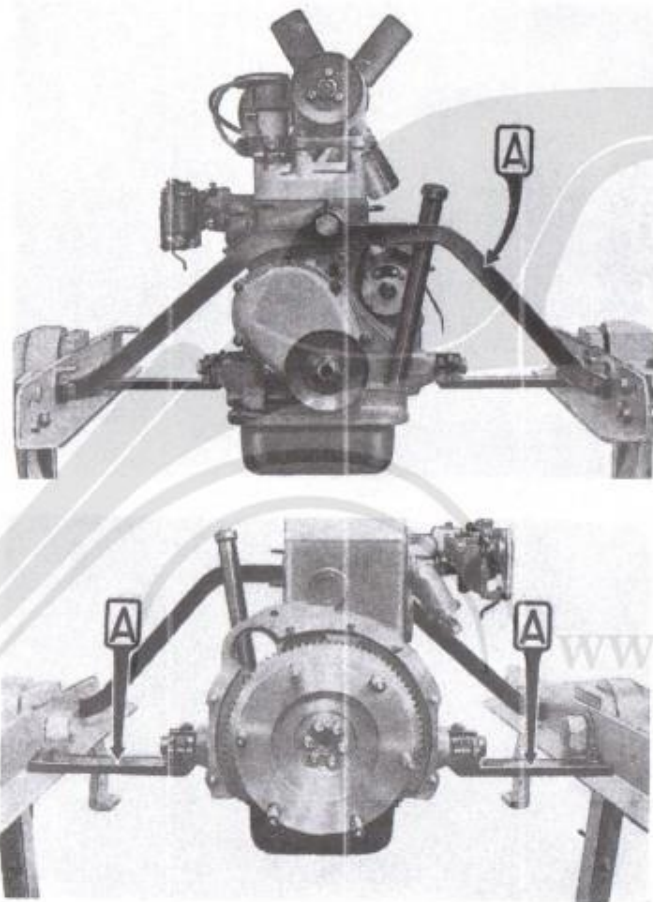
e 11. - A - Staffe Arr. 2205/X, per il fissaggio del motore al cavalletto rotativo Arr. 2204.
